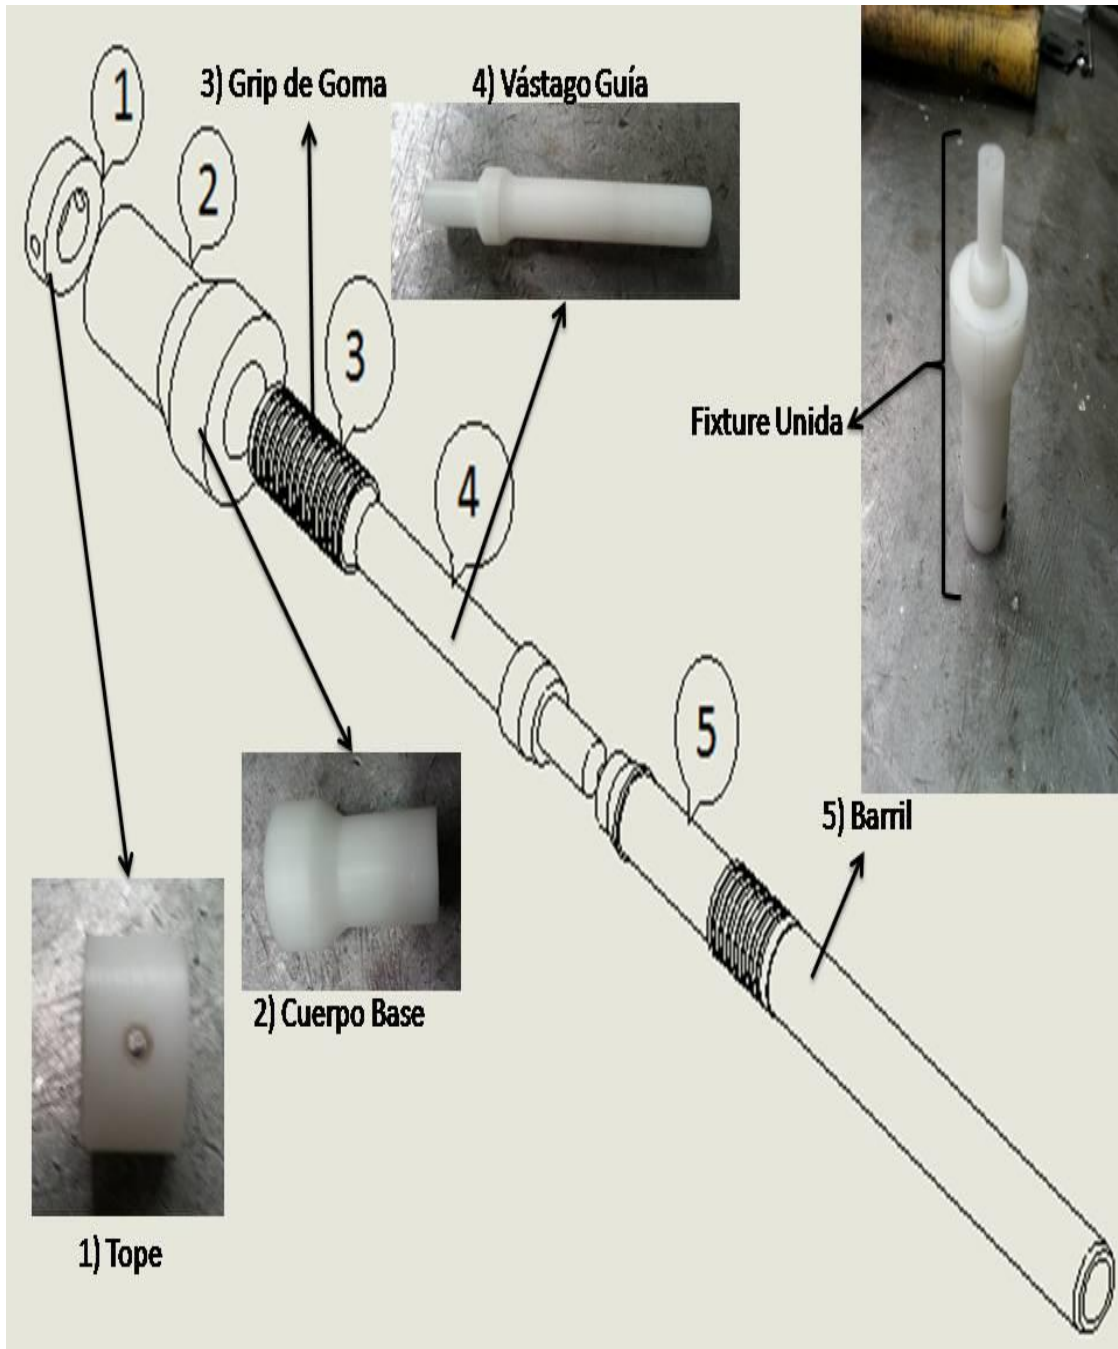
Dibujo Explosionado para el conjunto de trabajo de la fixture. 1) Abrazadera de guía. 2) Cuerpo de fixture. 3) Grip, 4) Guía de grip 5) Barril.
